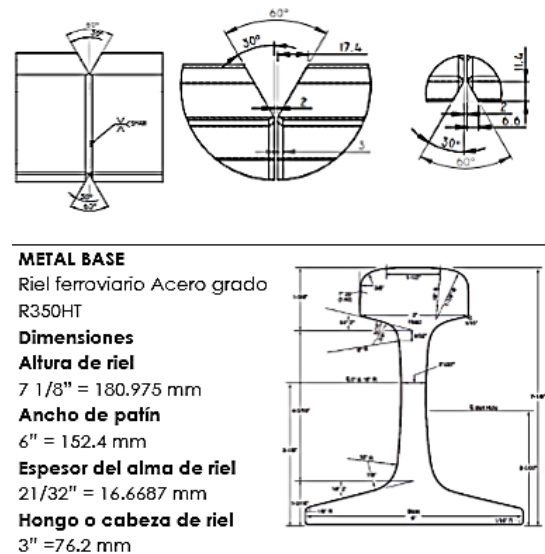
Diseño de junta para soldadura de riel ferroviario.
